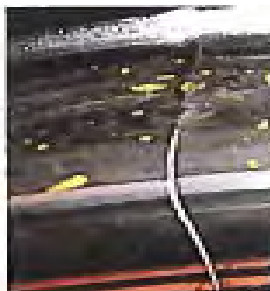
Fisuras laterales por sobrecargas térmicas
